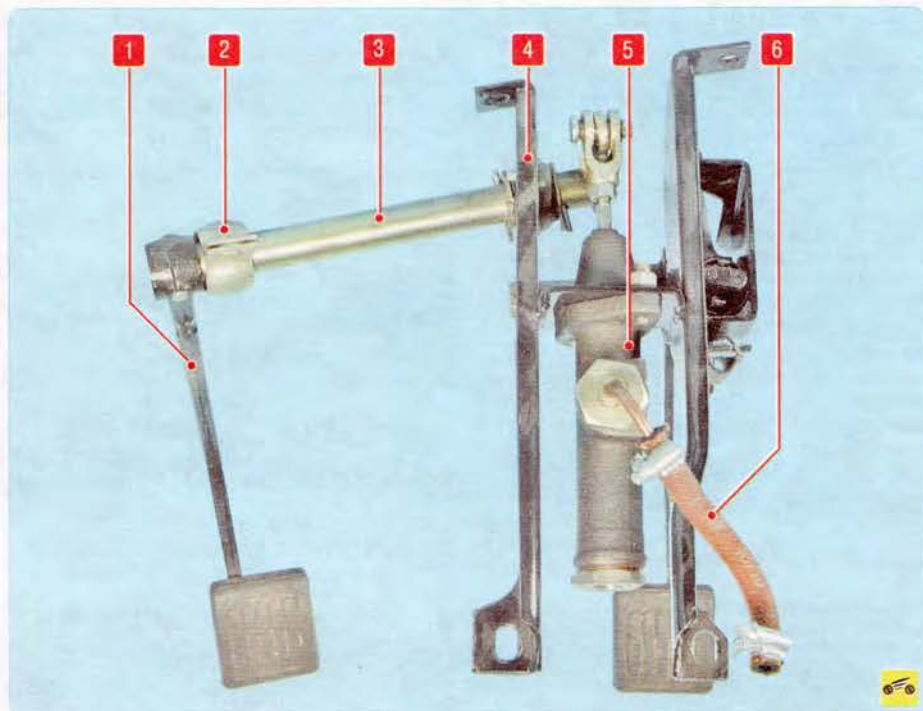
Главный цилиндр и педаль привода выключения сцепления: 1 – педаль сцепления; 2 – кронштейн крепления оси педали сцепления; 3 – ось педали сцепления; 4 – кронштейн педального узла; 5 – главный цилиндр гидропривода выключения сцепления; 6 – шланг бачка главного цилиндра гидропривода выключения сцепления
